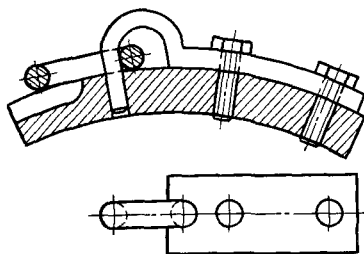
Крепление сварной цепи к барабану
